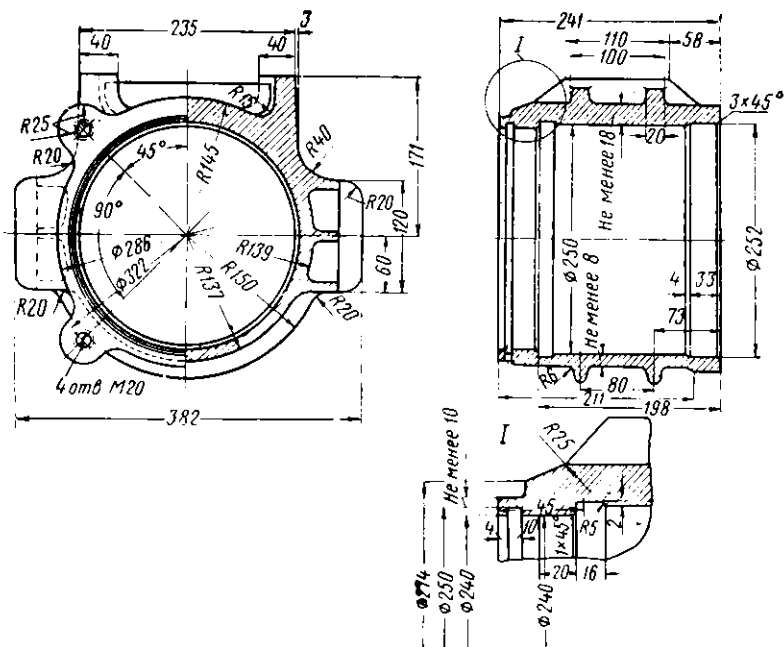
Корпус буксы для роликовых подшипников тележек грузовых вагонов
